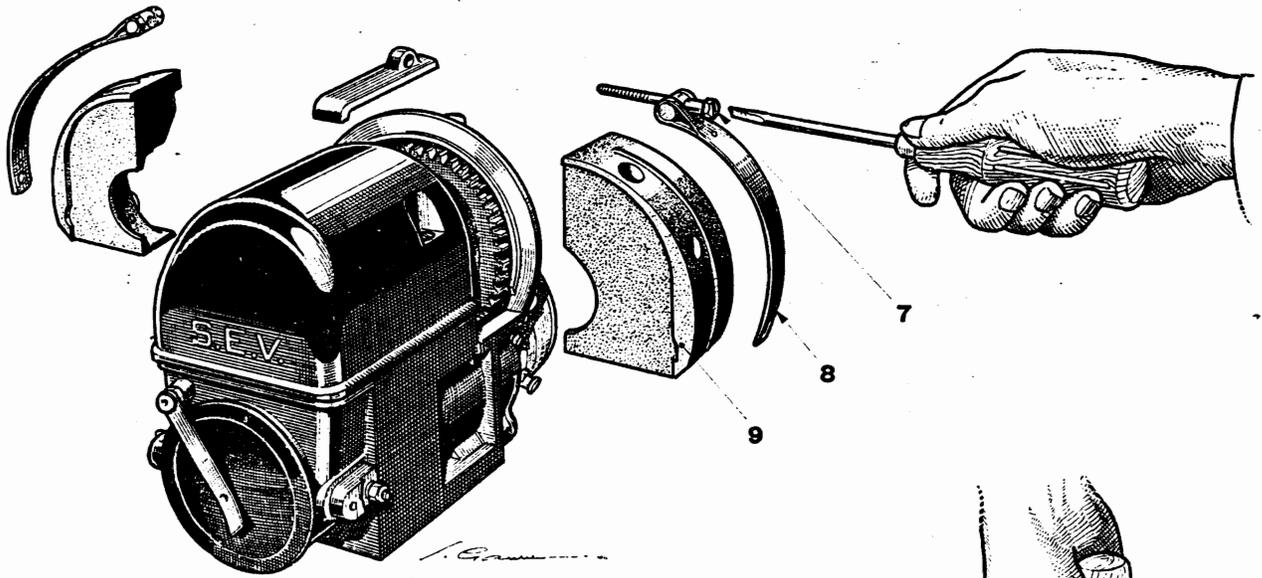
DÉMONTAGE DU DISTRIBUTEUR
